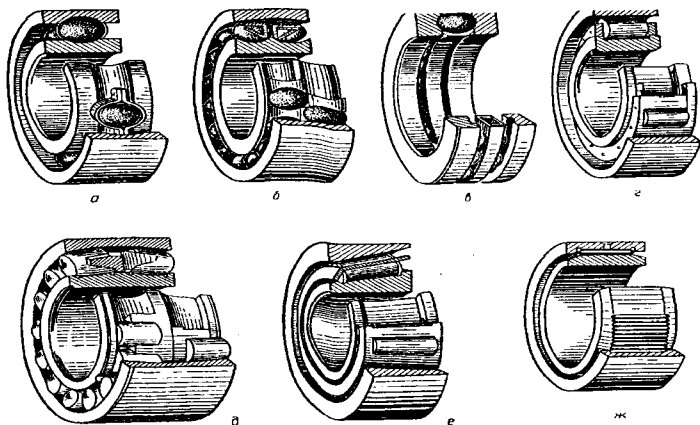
Подшипники качения: а – радиальный однорядный шариковый; б – шариковый двухрядный радиальный; в – шариковый упорный; г – роликовый двухрядный сферический (самоустанавливающийся); д – конический радиально-упорный; ж – игольчатый (радиальный).
